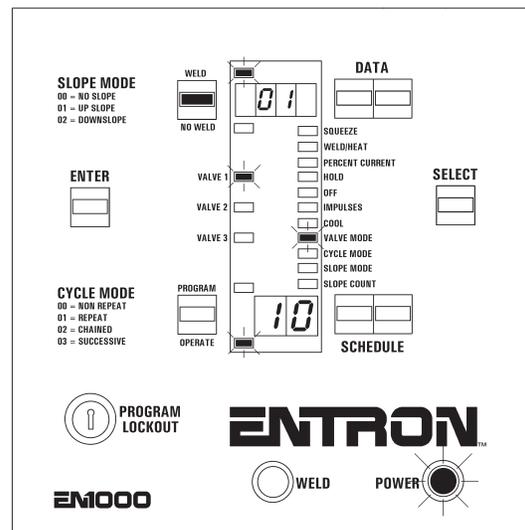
Ponga el control en modo SOLDAR (WELD)
